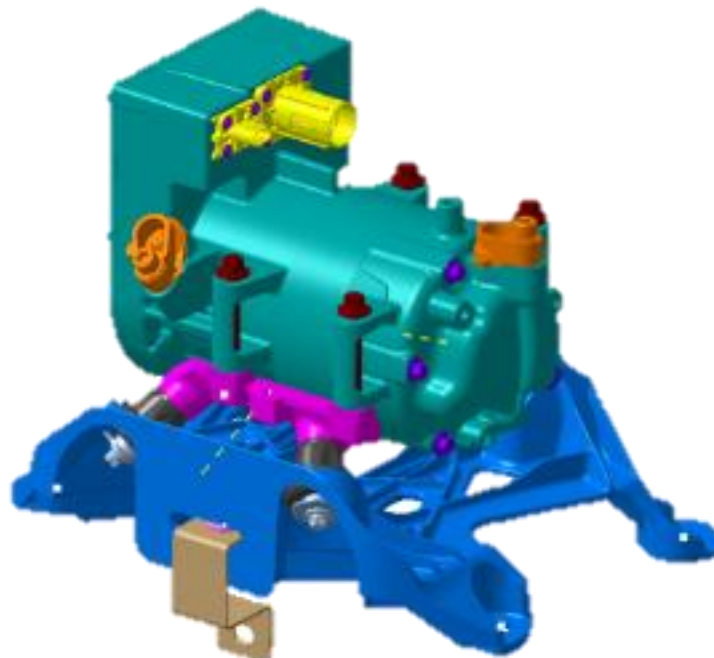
Sub-montagem do compressor com a *Motor Housing 800V* incluída
